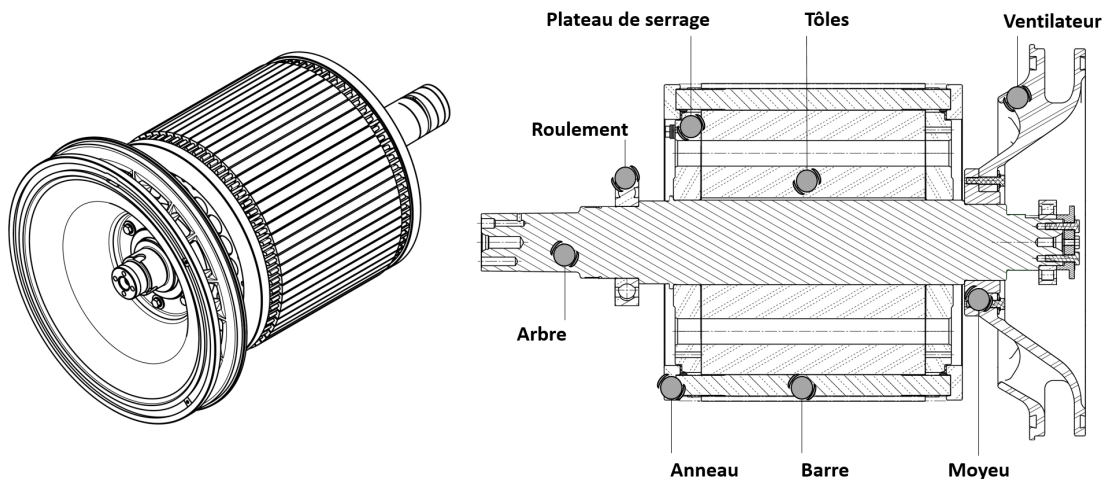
Vue en perspective et en coupe d'un rotor de moteur asynchrone
